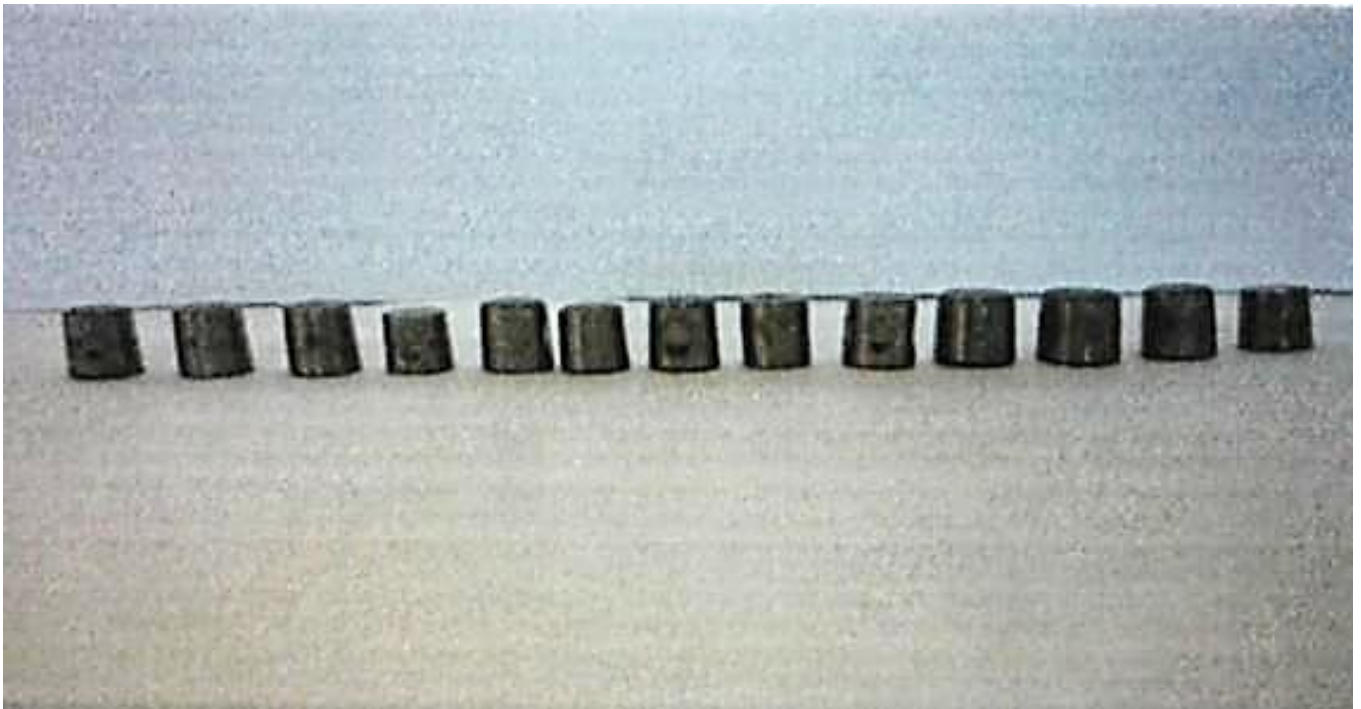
Ролики подшипника - образцы с различной степенью износа
